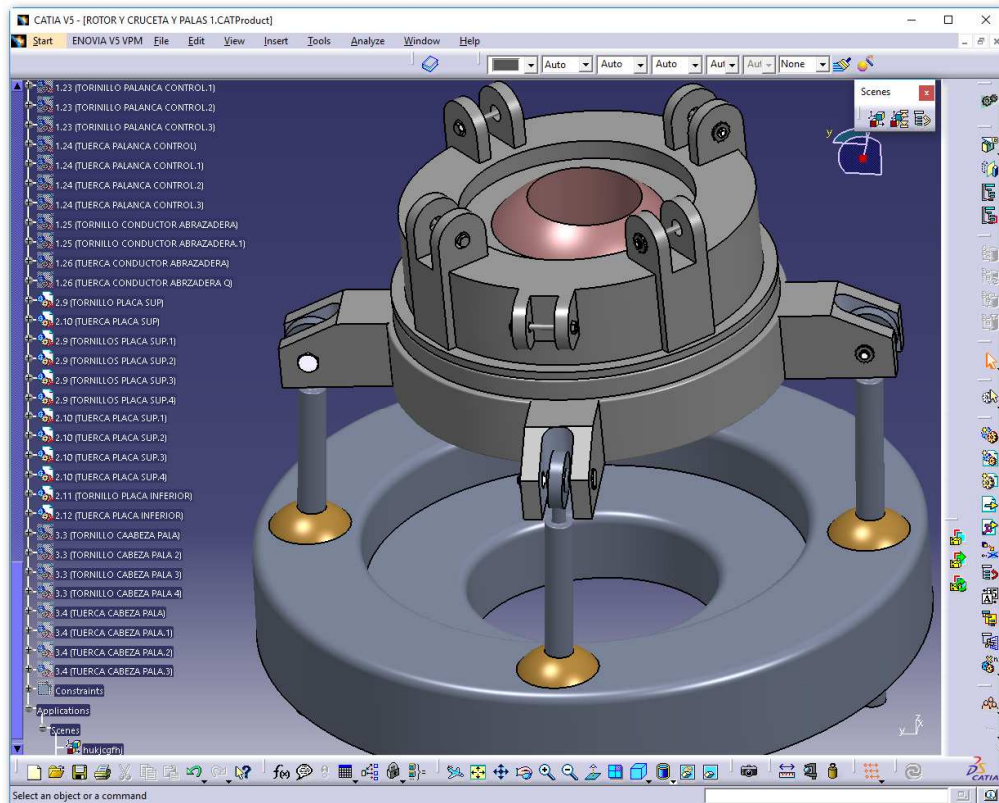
Conjunto sistema placa oscilante.
